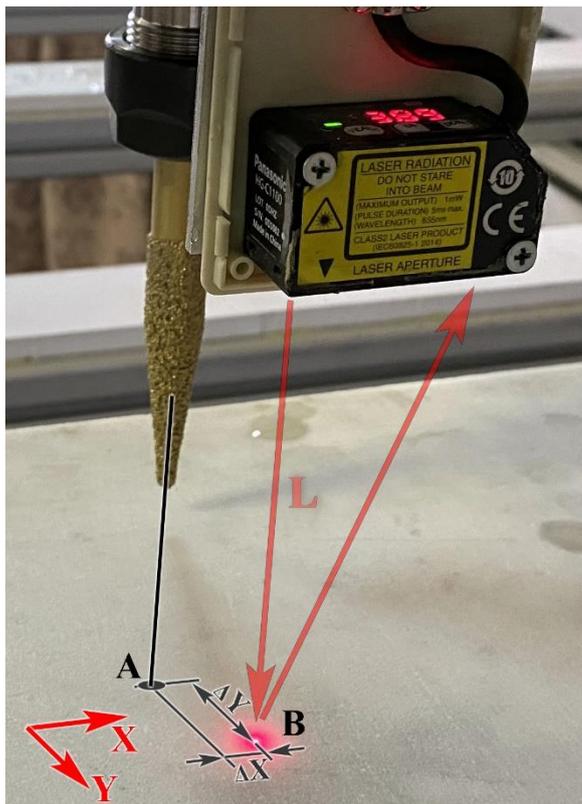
Смещение лазерного сканера относительно фрезы.
